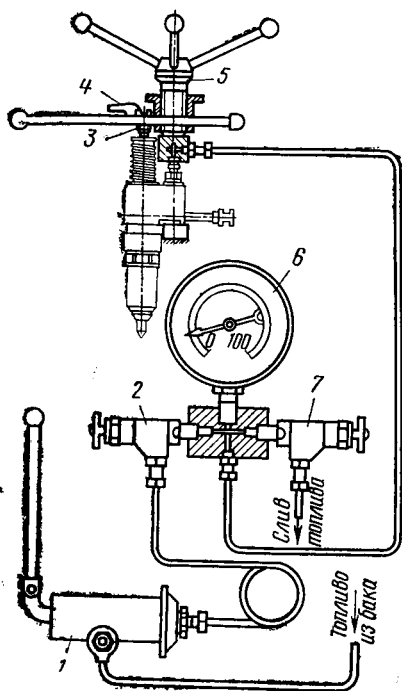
Схема гидравлического стенда для проверки насос-форсунки: 1 — насос высокого давления; 2 — запорный клапан; 3 — регулировочный винт; 4 — защелка; 5 — прижим; 6 — манометр; 7 — спускной кран
